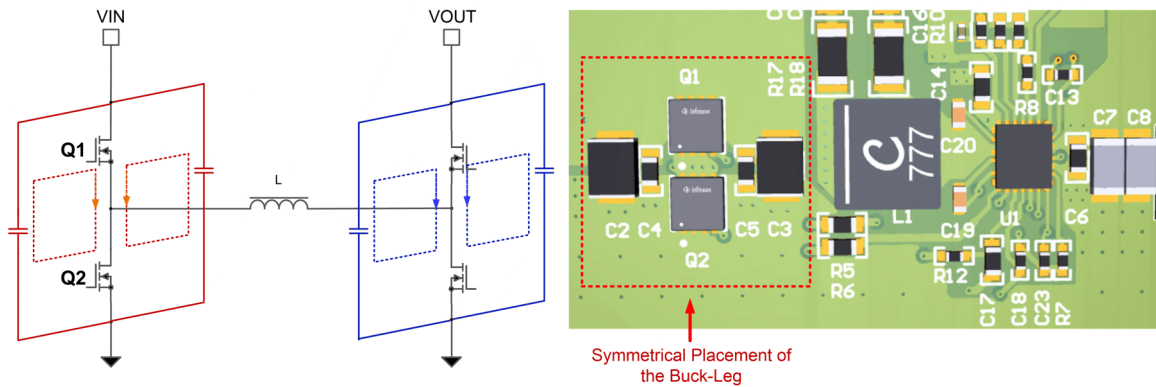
TPS55288 降压/升压转换器的对称 PCB 布局
